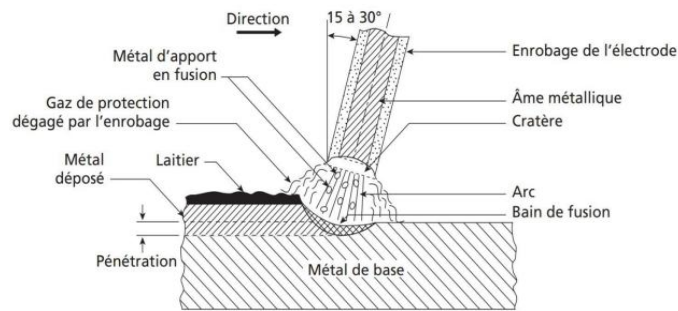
Principe de soudage à l'arc avec électrode enrobée. [29]
